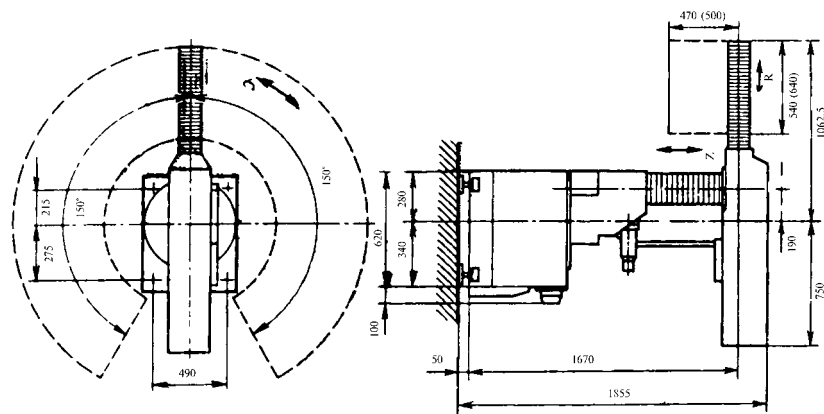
Общий вид промышленного робота Faber C 5000 с цилиндрической системой координат
